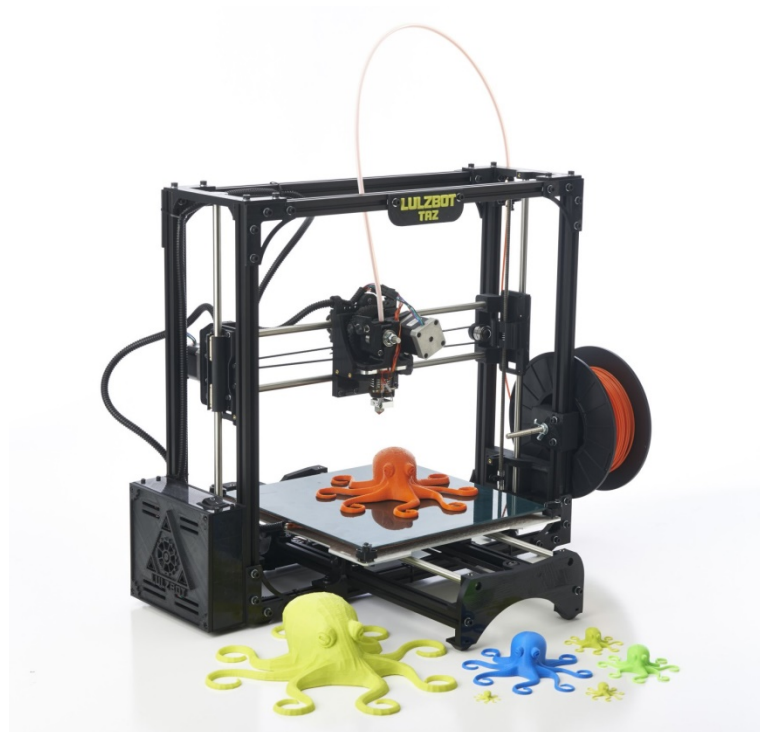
Impresora 3D de estructura tipo pórtico
